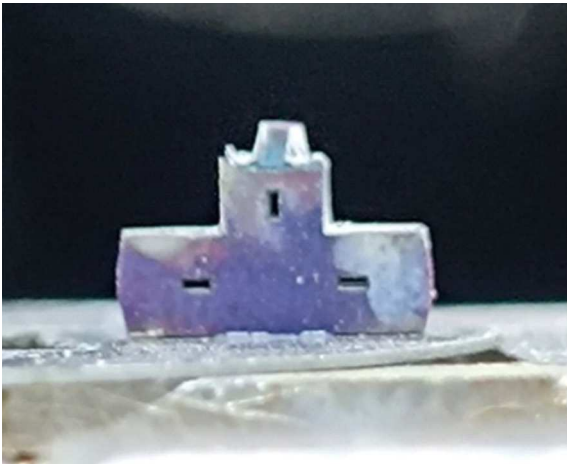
Фотография заготовки в виде крестовины с изготовленным катодным выступом.
